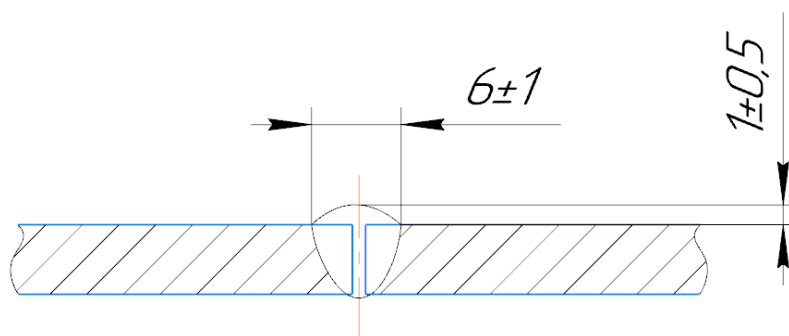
Геометрические параметры сварного шва
